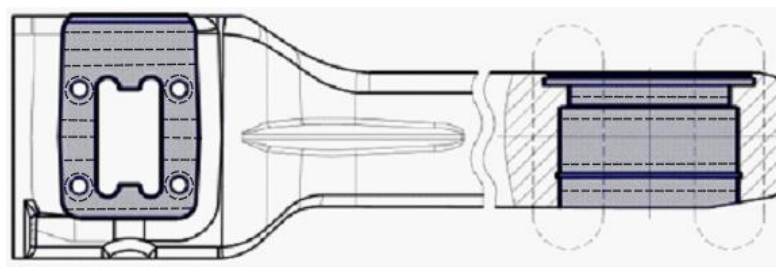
Схема сканирования корпуса сцепки
